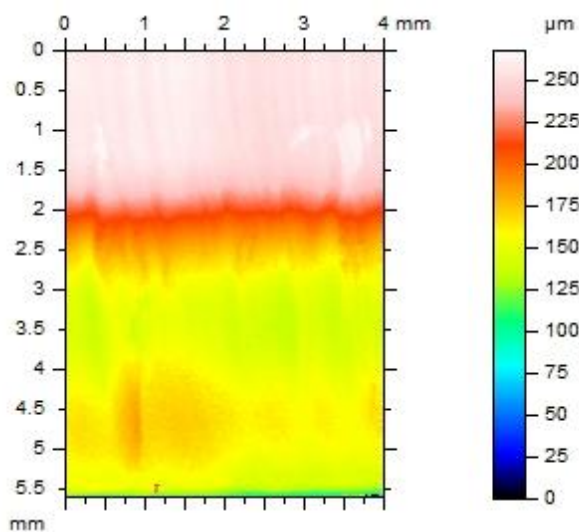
Drsnost obrobeného povrchu materiálu 11 373 tloušťka 5 mm s odfiltrovanou vlnitostí, obrábění plazmou
